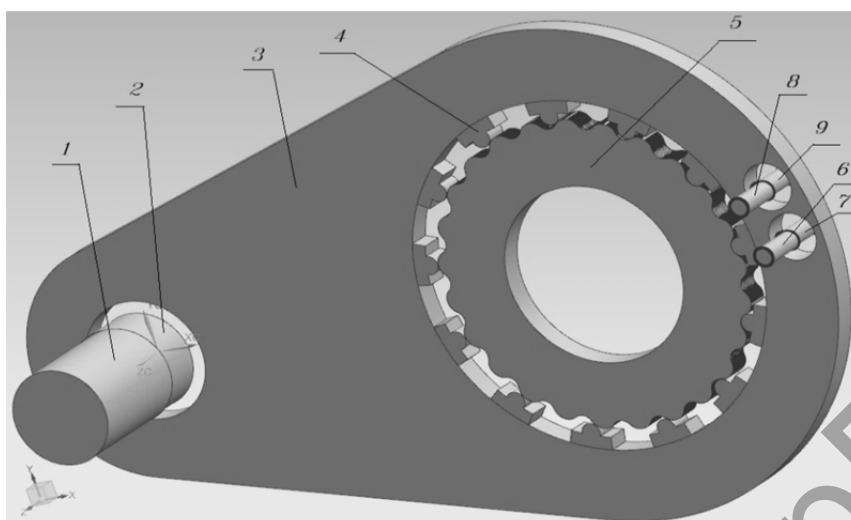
Компьютерная модель эксцентриковой передачи с параллельным расположением входного и выходного валов с дополнительными кривошипами 7 и 9, вращающимися на валах 6 и 8
